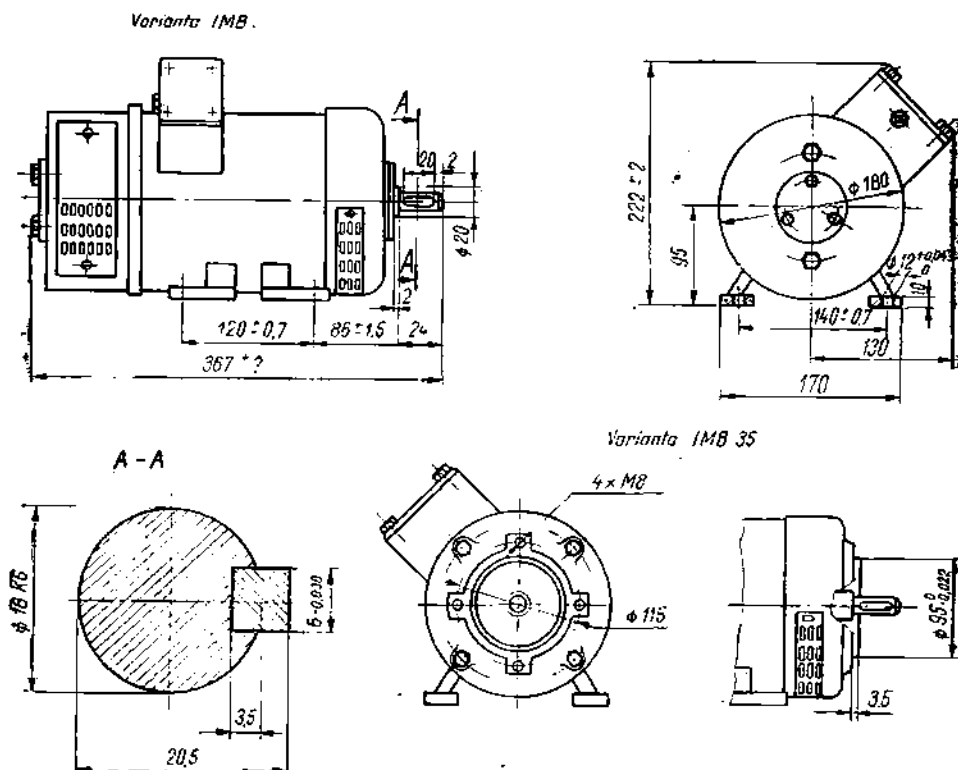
Motor tip Ce 12—1,9 kW. Dimensiuni de montaj.
